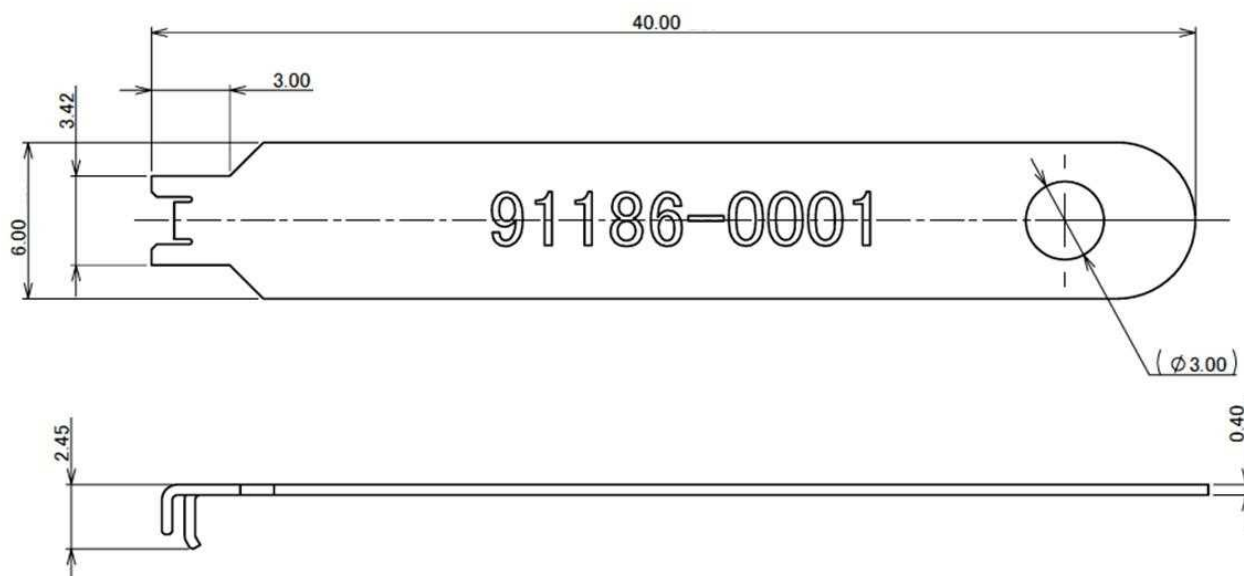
推奨 挿抜 JIG (Recommended mating and unmating JIG)
